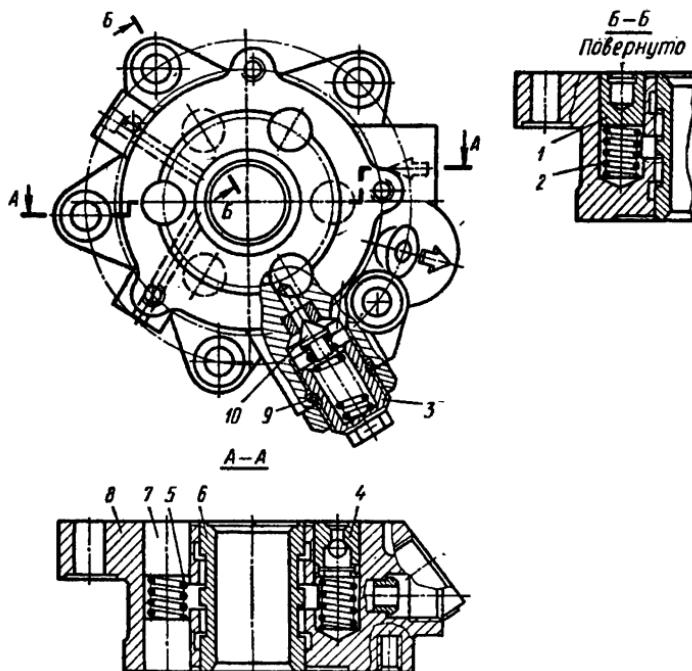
Клапан управления гидроусилителем рулевого привода:
